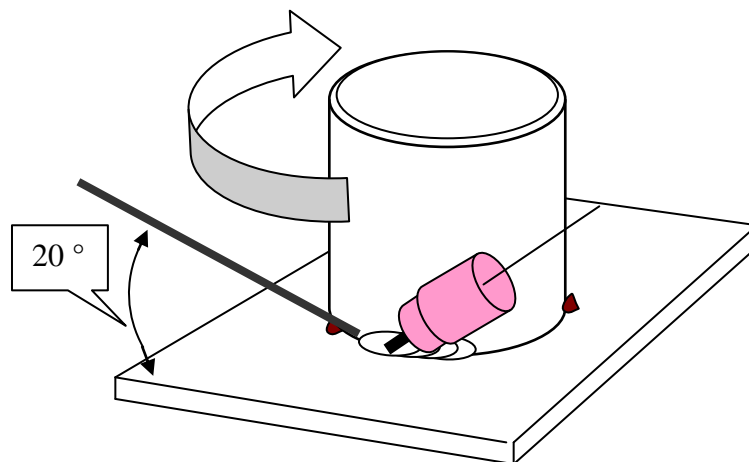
Realización de la soldadura de tubo sobre placa en posición plana, con aporte.
